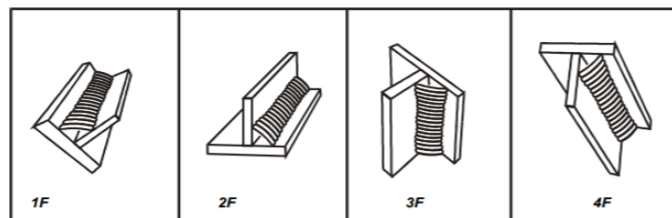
Diferentes vistas de una soldadura de tope [44].
